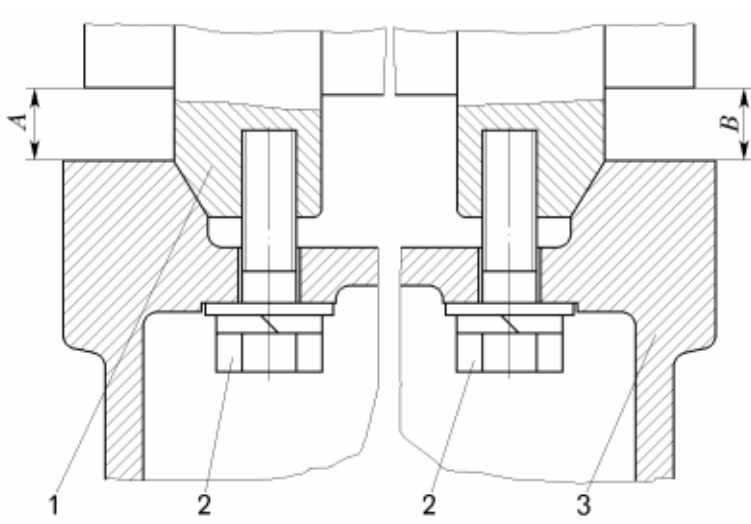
Крепление гидроцилиндра к кронштейну балки передней оси:
